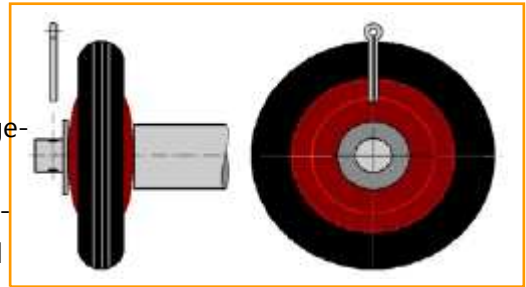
Fijación de una rueda mediante pasador de aletas.
